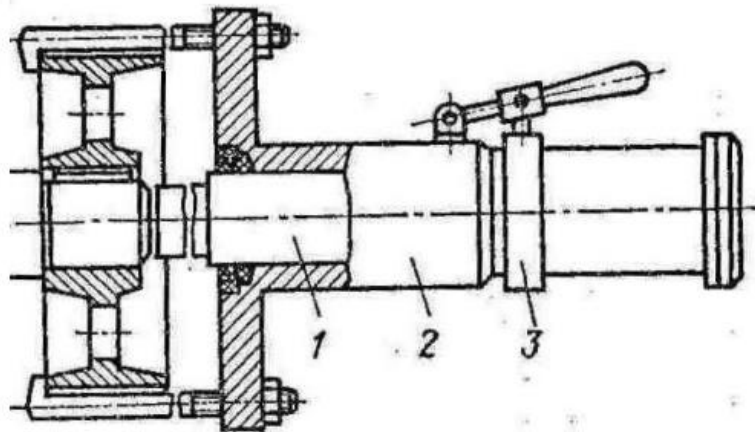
Загальний вигляд ручних пристроїв гідравлічного типу: 1 – поршень; 2 – циліндр; 3 – плунжерний насос.
